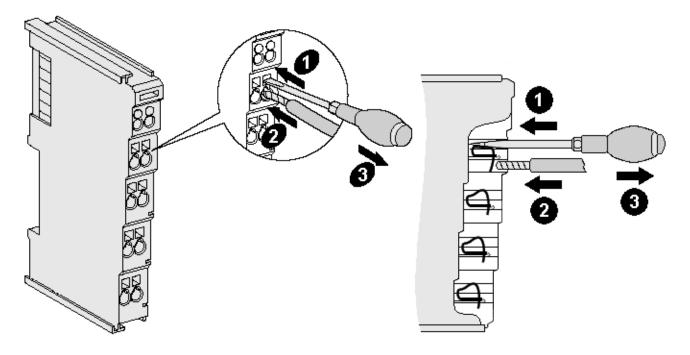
Anschluss einer Leitung an eine Klemmstelle
